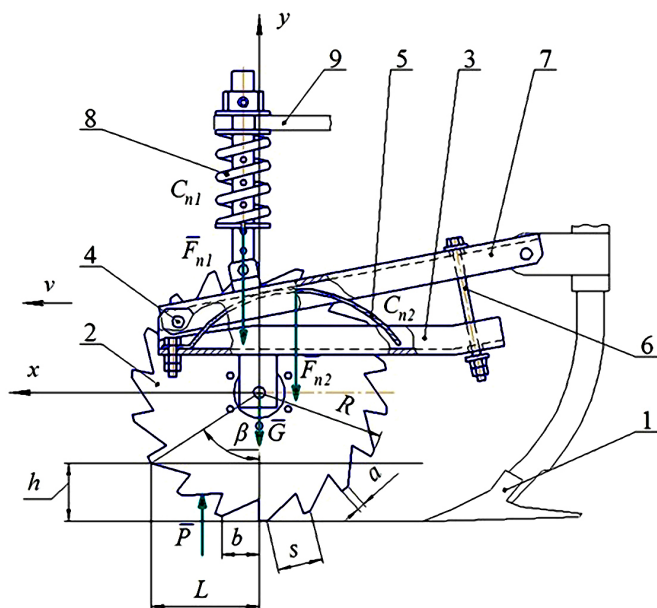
Эквивалентная схема комбинированного рабочего органа плоскорезного культиватора к обоснованию параметров пружиненного зубчатого диска
